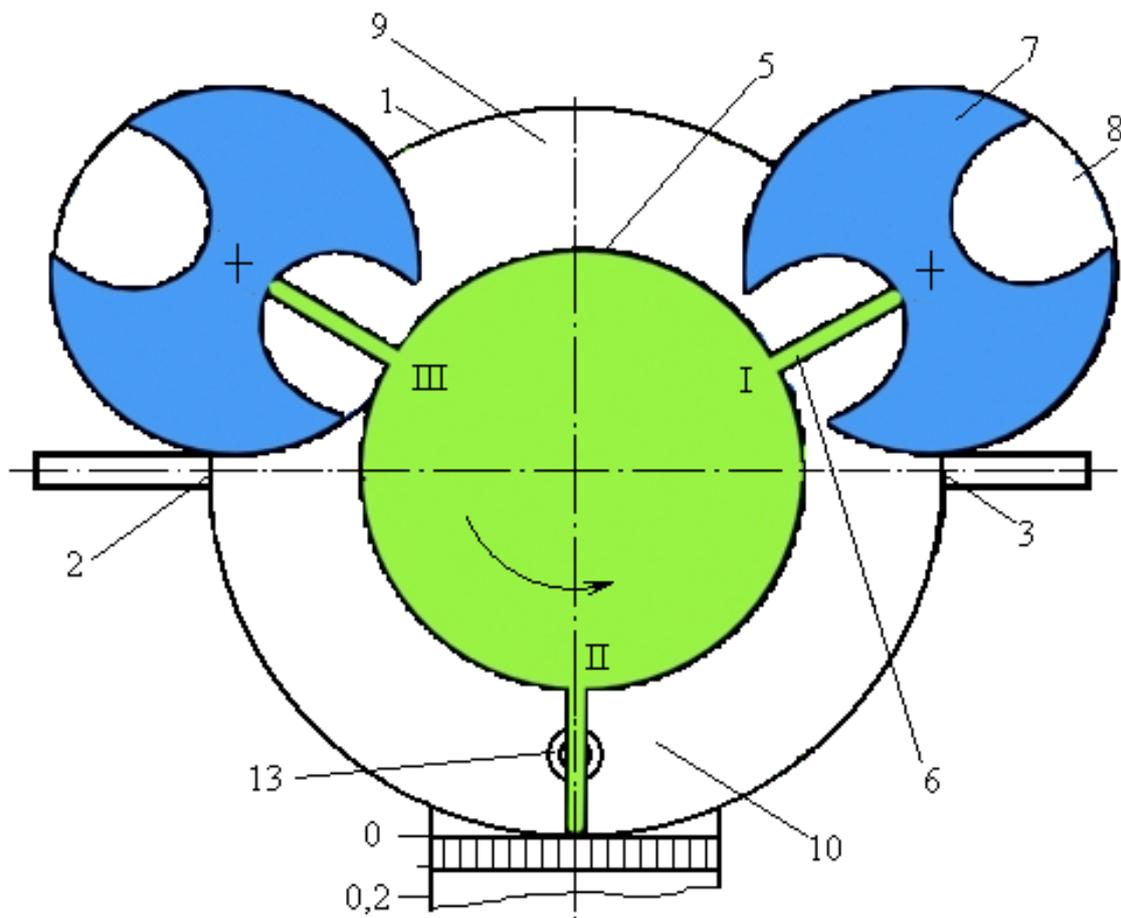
Схема положения деталей КШМ в момент прохождения поршнем верхней мертвой точки
